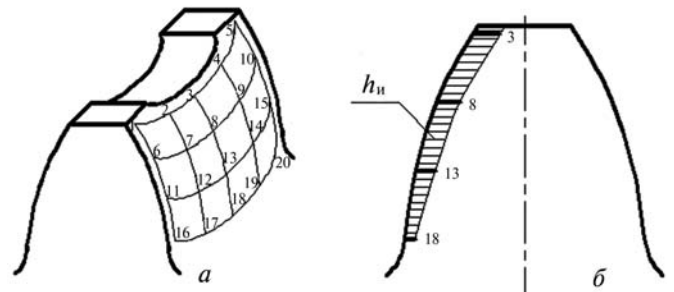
Сетка для замеров величин износа (а) и форма боковой поверхности изношенного (б) зуба червячного колеса
